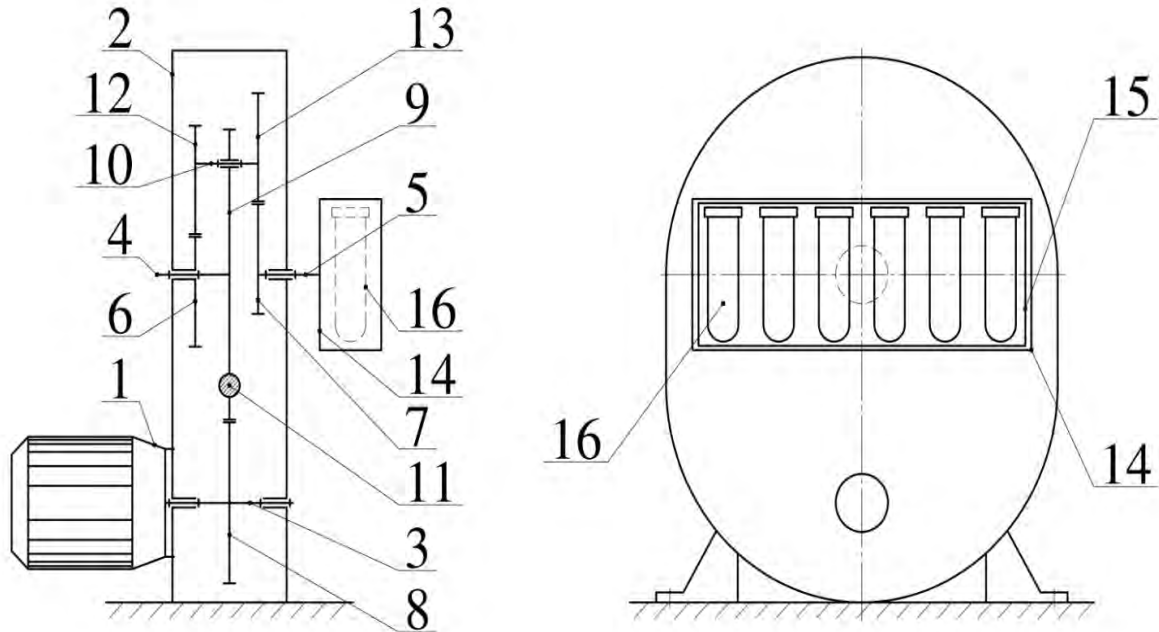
Лабораторный встряхиватель с возвратно-вращательным движением держателя с пробирками: 1 – электродвигатель; 2 – корпус; 3 – входной вал; 4 – промежуточный вал; 5 – выходной вал; 6 – неподвижное эллиптическое зубчатое колесо; 7 – эллиптическое колесо на выходном валу; 8 – цилиндрическое зубчатое колесо; 9 – водило; 10 – вал сателлита; 11 – противовес; 12, 13 – эллиптические зубчатые колеса сателлита; 14 – выходное звено; 15 – держатель для пробирок; 16 – пробирки с образцами
